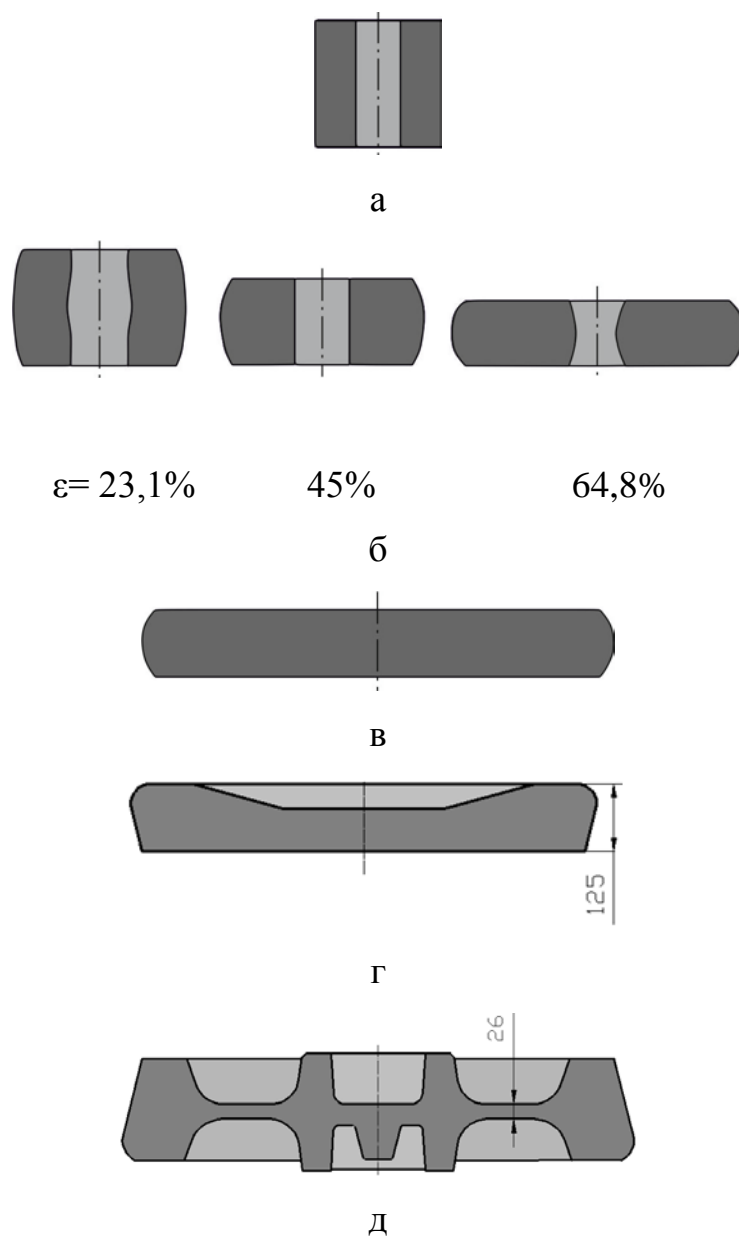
Формоизменение металла при деформировании полый заготовки на прессах ($D=460$ мм, $H= 447$ мм, $d= 160$ мм): а- исходная полая заготовка, б, в – свободная осадка, г- осадка и разгонка в технологическом кольце, д- формовка
